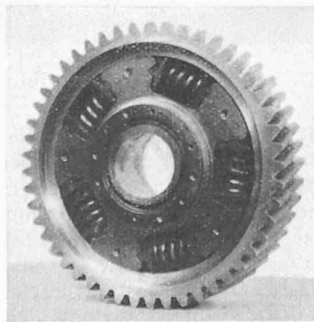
Gefederter Zahnkolben der Triebmotoren.
